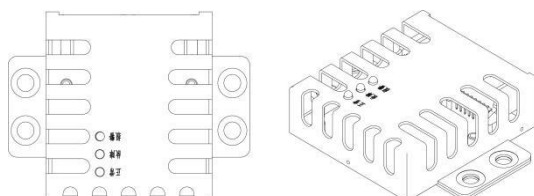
Зовнішній вигляд композитного газового датчика
